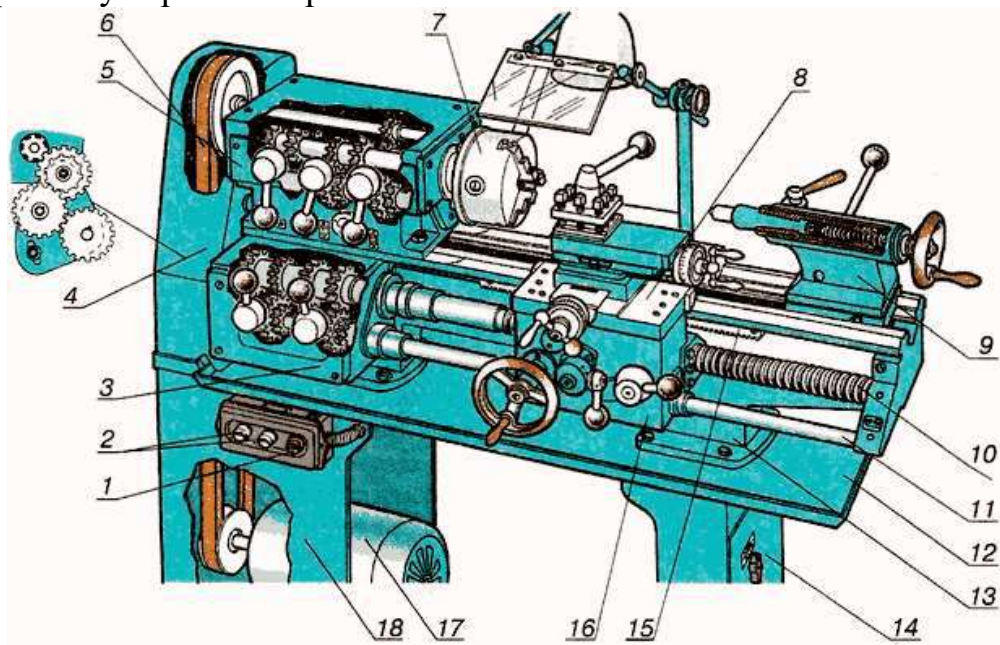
Будова токарно-гвинторізного верстату ТВ-6
